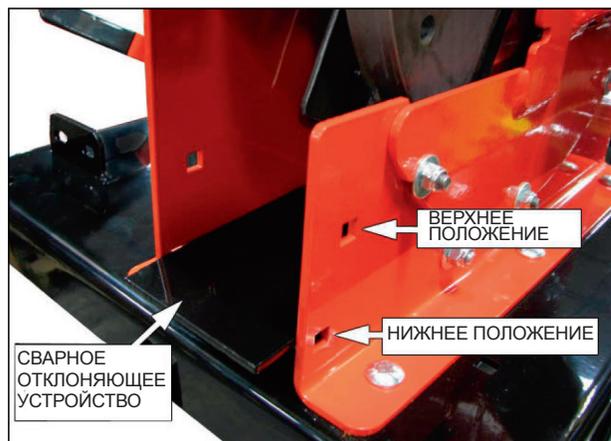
Сварное отклоняющее устройство измельчителя
